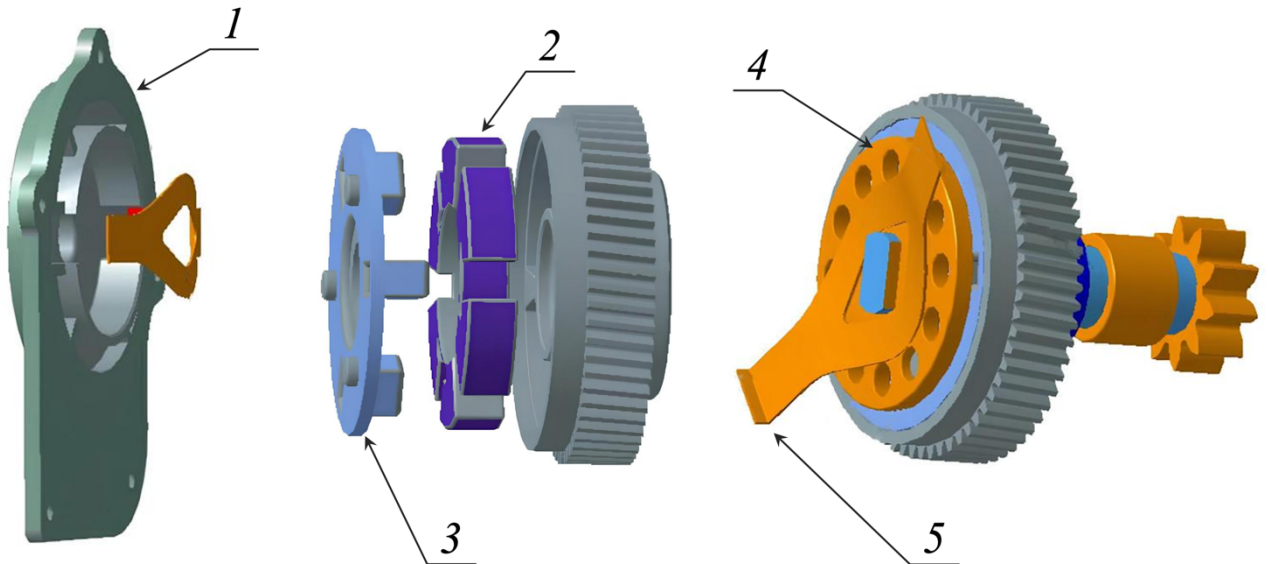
Конструкция механизма аварийного расцепления:
